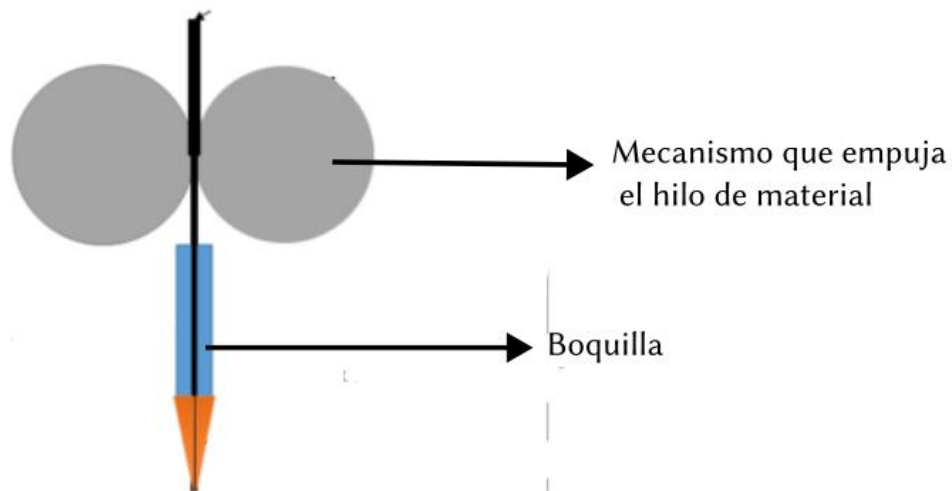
Esquema de una boquilla de una máquina de impresión 3d. Fuente: [21]
